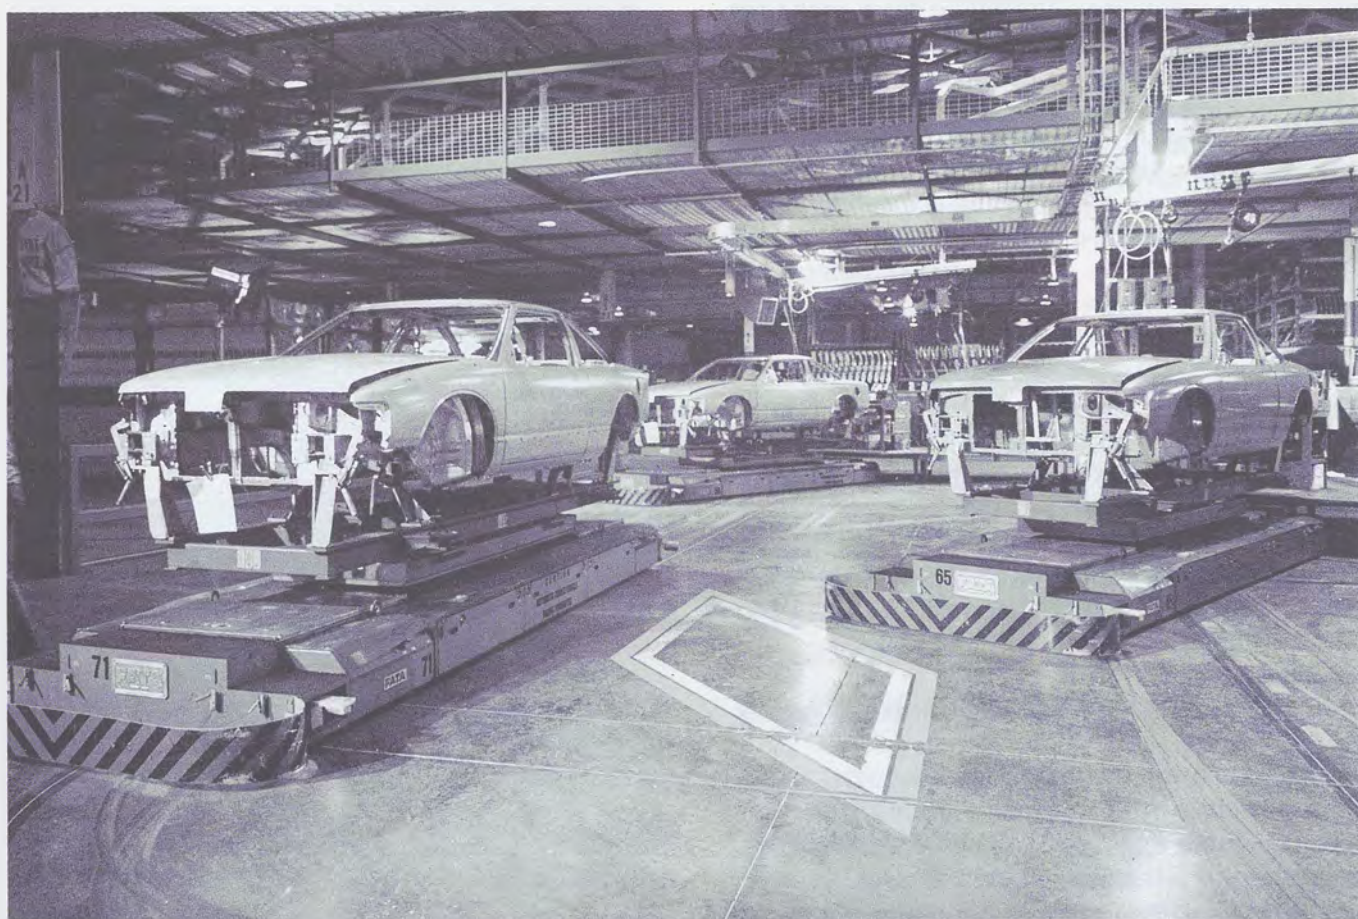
AGV per FAS - linea di assemblaggio scocche.
